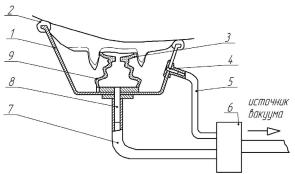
Схема устройства для массажа вымени животных однокамерного типа: 1 – кожух; 2 – уплотняющая прокладка; 3 – присосок; 4, 8 – патрубки; 5, 7 – шланги; 6 – пульсатор; 9 – пневмокамера
